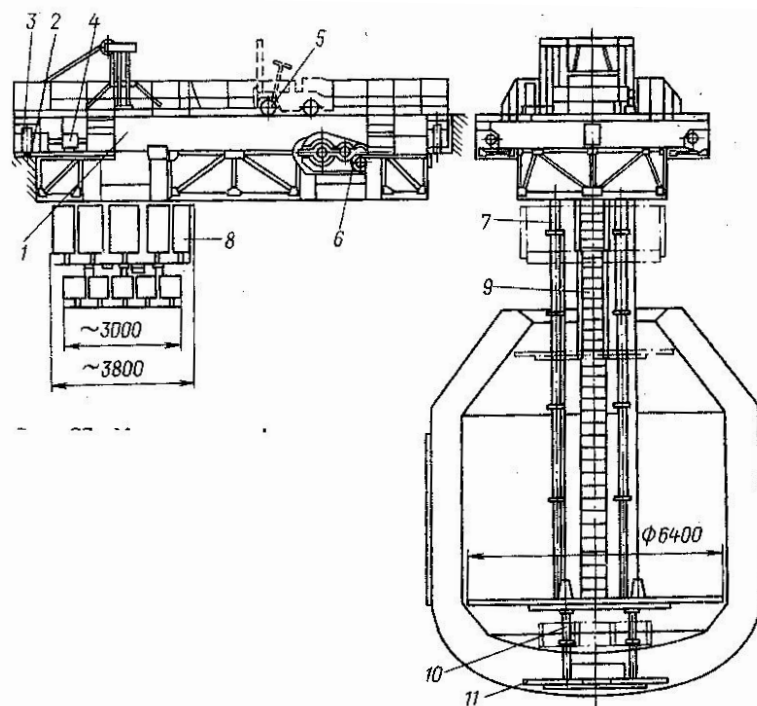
Телескопическая машина для кладки футеровки конвертера с цельным корпусом:
